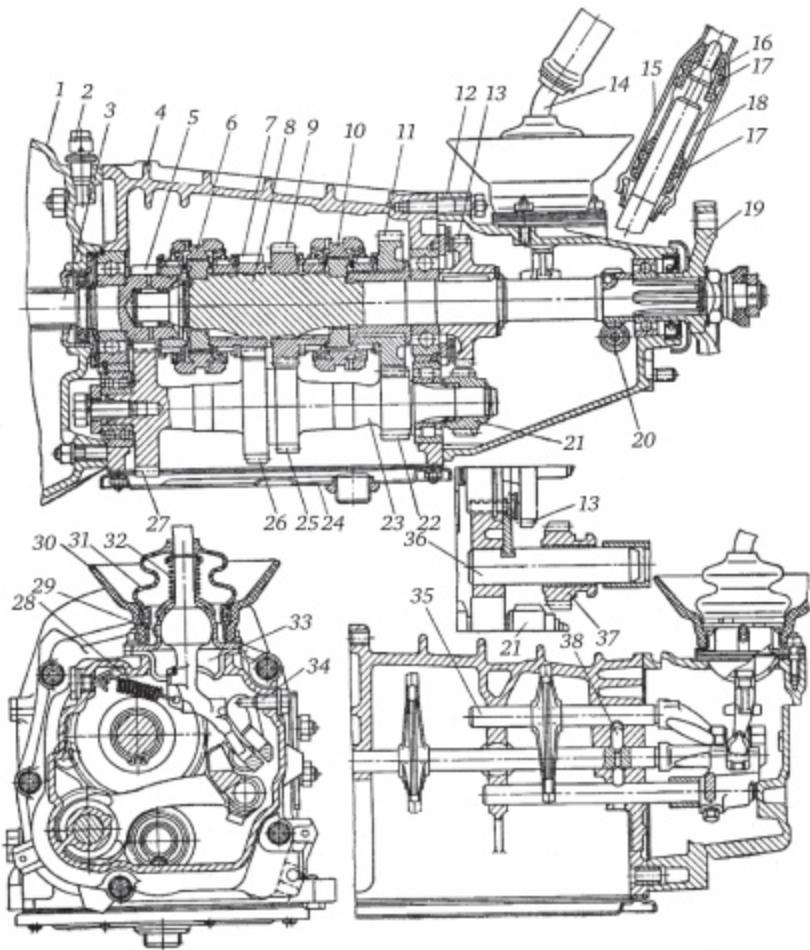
3-вальная 4-ступенчатая коробка передач с шестернями заднего хода, расположенные в полости задней крышки
